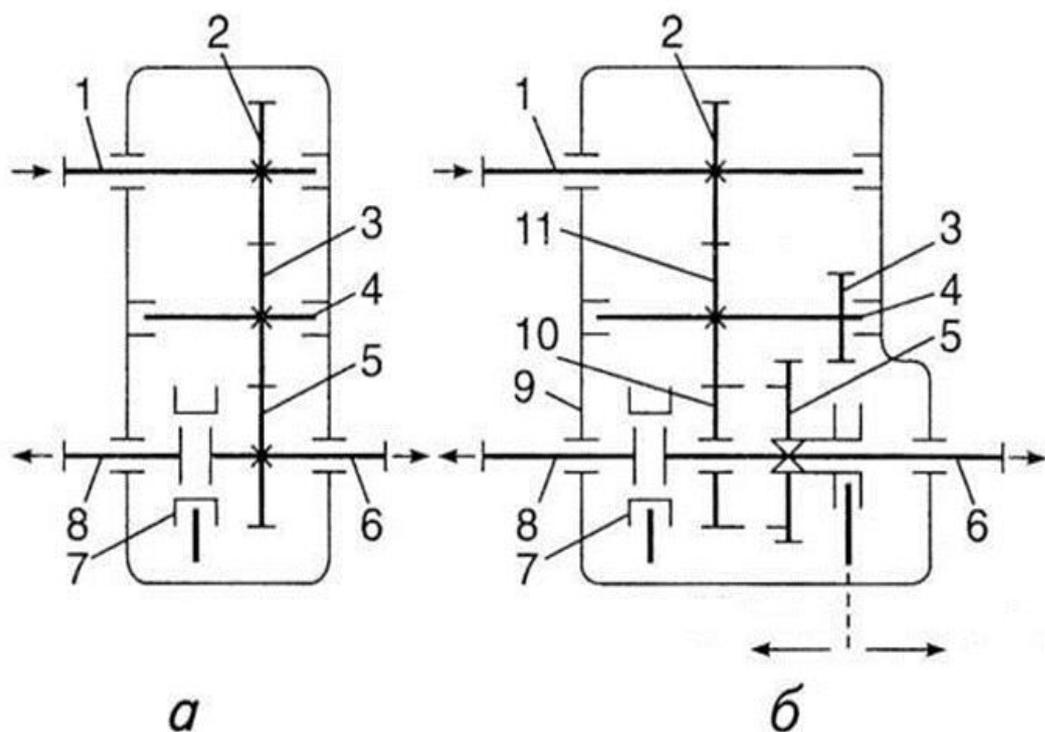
Схемы раздаточных коробок: а – без понижающей передачи; б – с понижающей передачей
